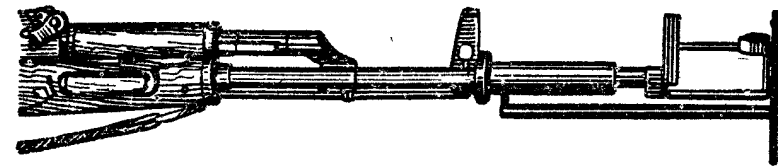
Крепление стрелково-тренировочного прибора конструкции Раффе на автомате
